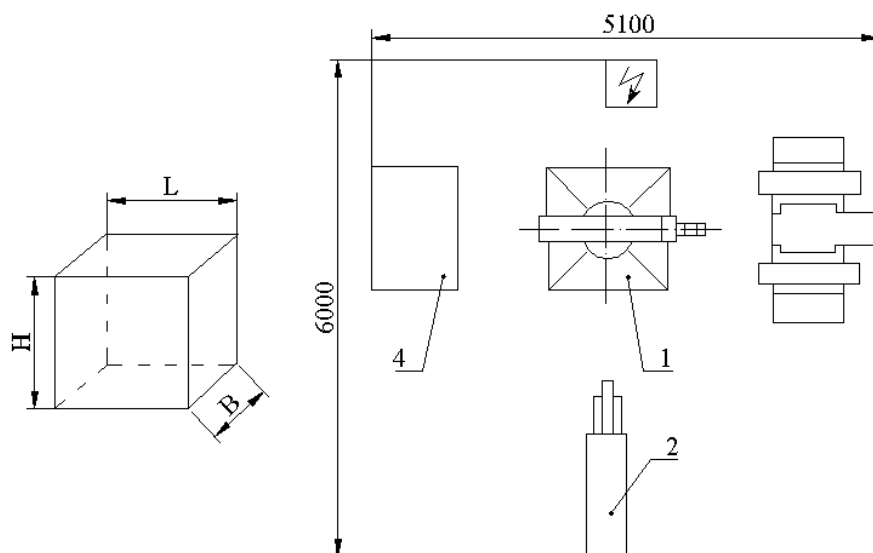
1 - ПР мод. РБ - 110; 2 - автомат точечной сварки; 3 - устройство гибки; 4 - накопитель изделий после сварки (стеллаж).
